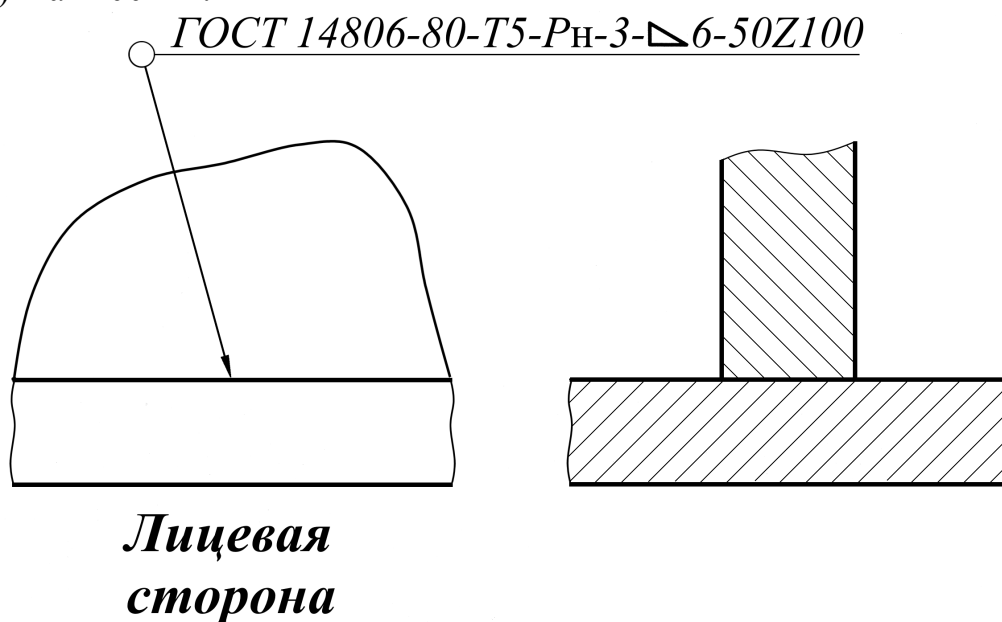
Условные обозначения некоторых видов сварных швов
